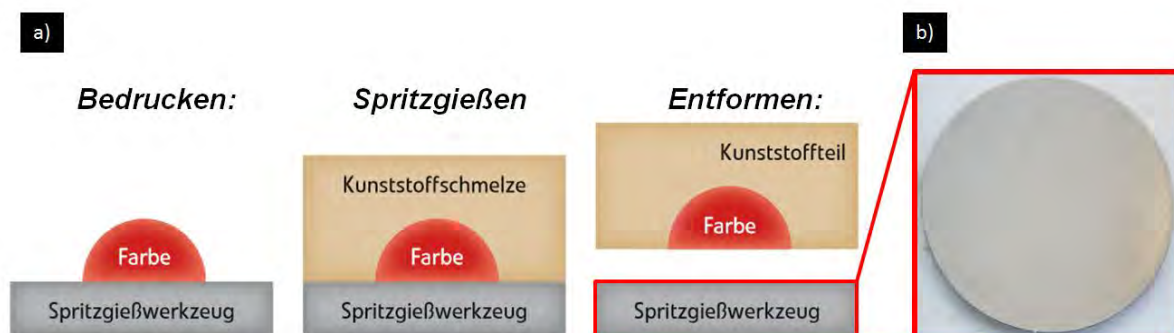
a) Schematische Darstellung der Prozessschritte beim In-Mold Printing von Spritzgießformteilen [Hae13a]: Bedrucken des Werkzeugs mit modifizierter Farbe, Spritzgießen, Entformen des erstarrten Kunststoffteils aus dem Werkzeug; b) Edelstahlplatte als vorläufiges Modell der Werkzeugwand
